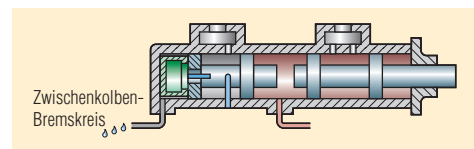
Tandem-Hauptzylinder mit defektem Zwischenkolben-Bremskreis.
